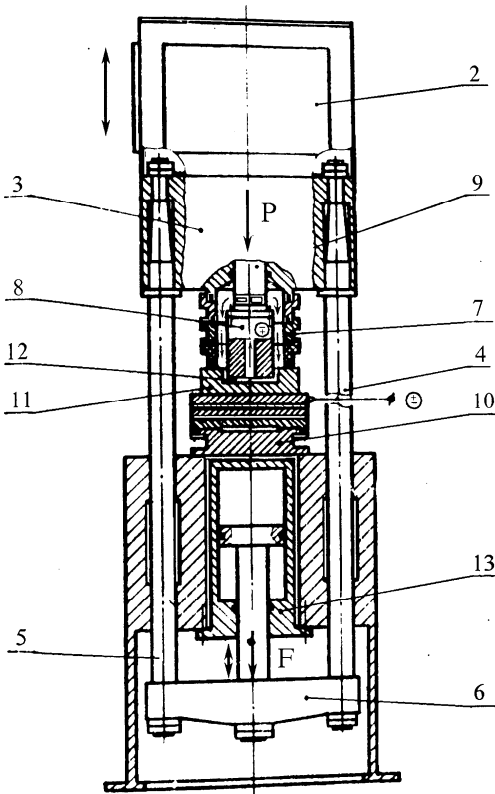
Кінематична схема верстату «Дуга – 8Д»
